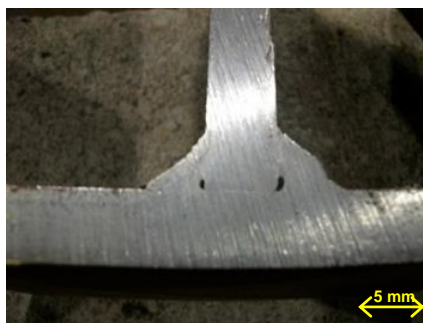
Falta de fusión en la raíz del cordón de soldadura (28)
